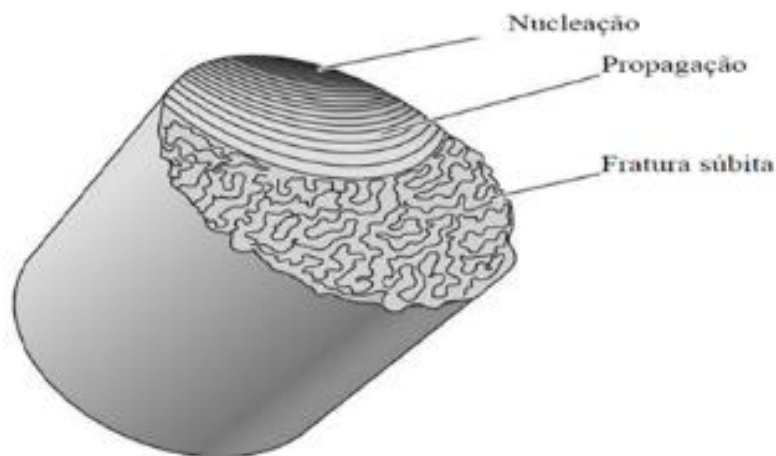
Representação esquemática de uma superfície de fratura por fadiga, [39].
